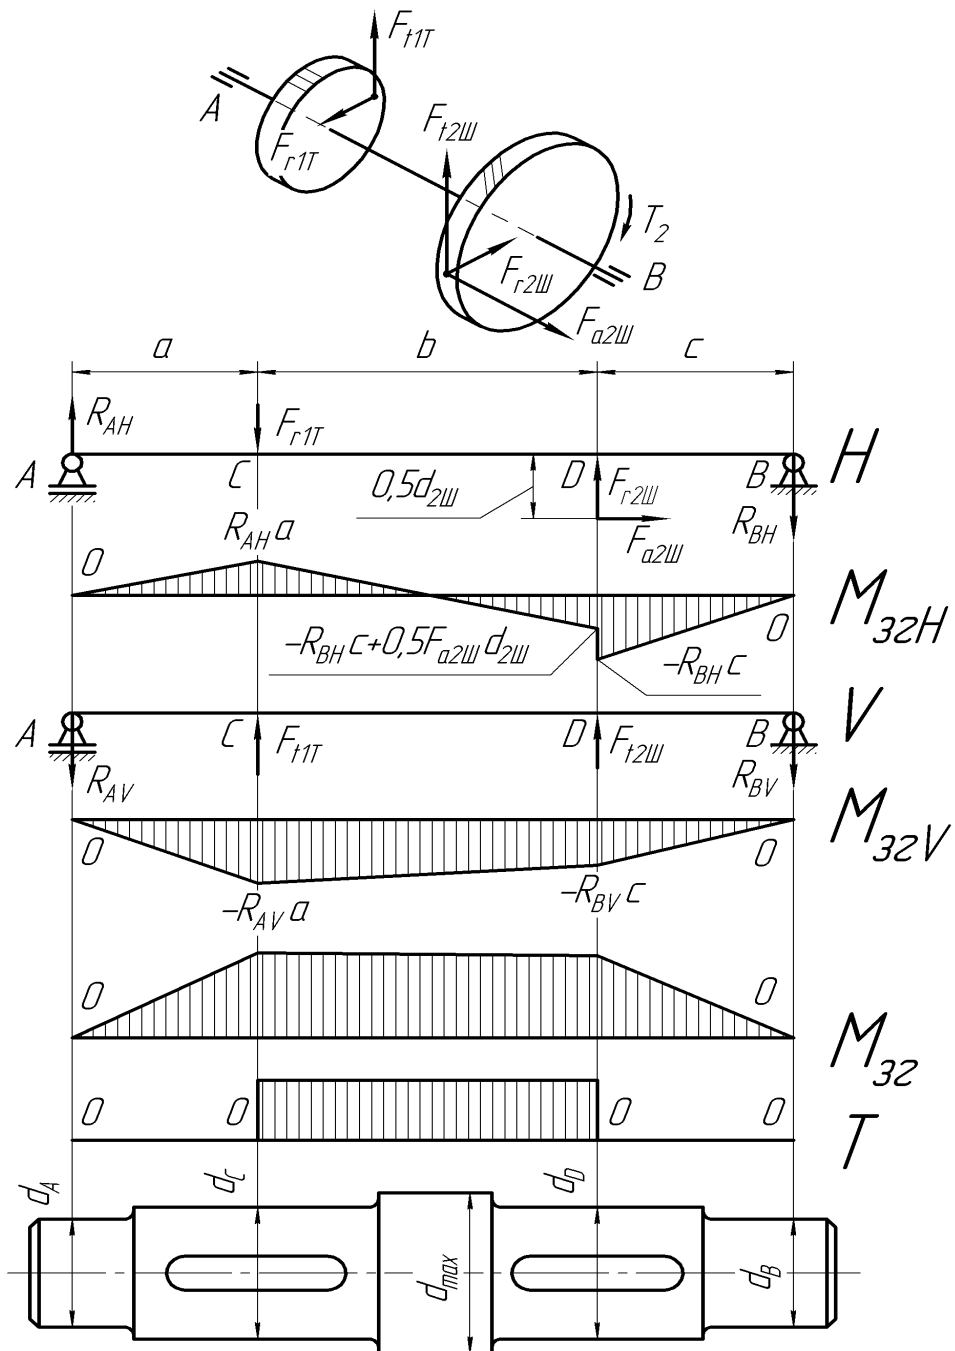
Розрахункова схема, епюри моментів і ескіз проміжного вала циліндричного двохступінчастого редуктора
